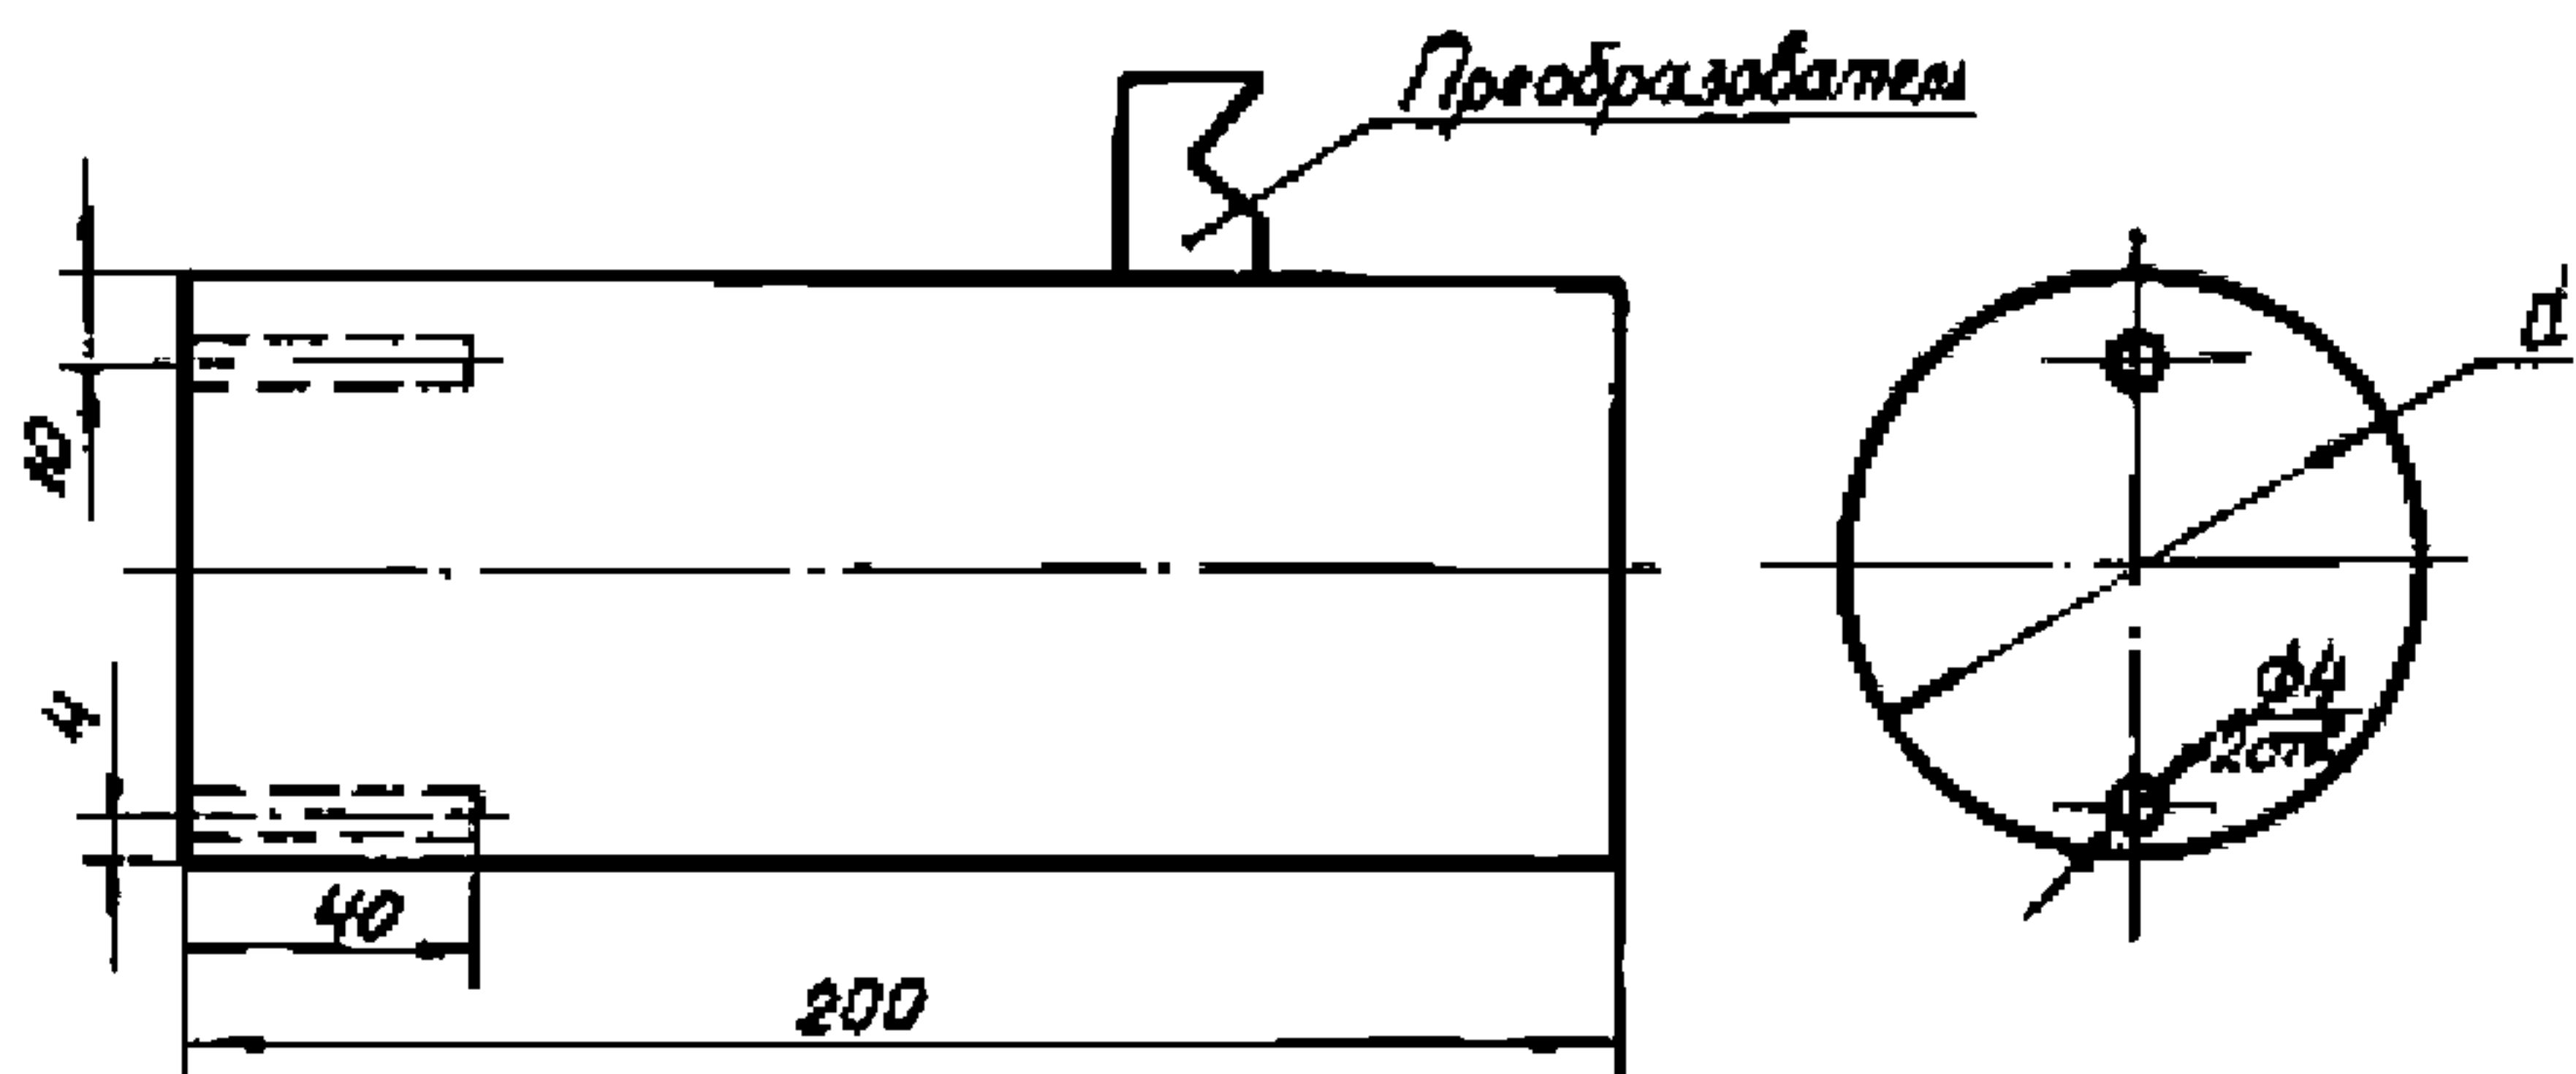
Стандартный образец для настройки ультразвукового прибора при НК штролов:
